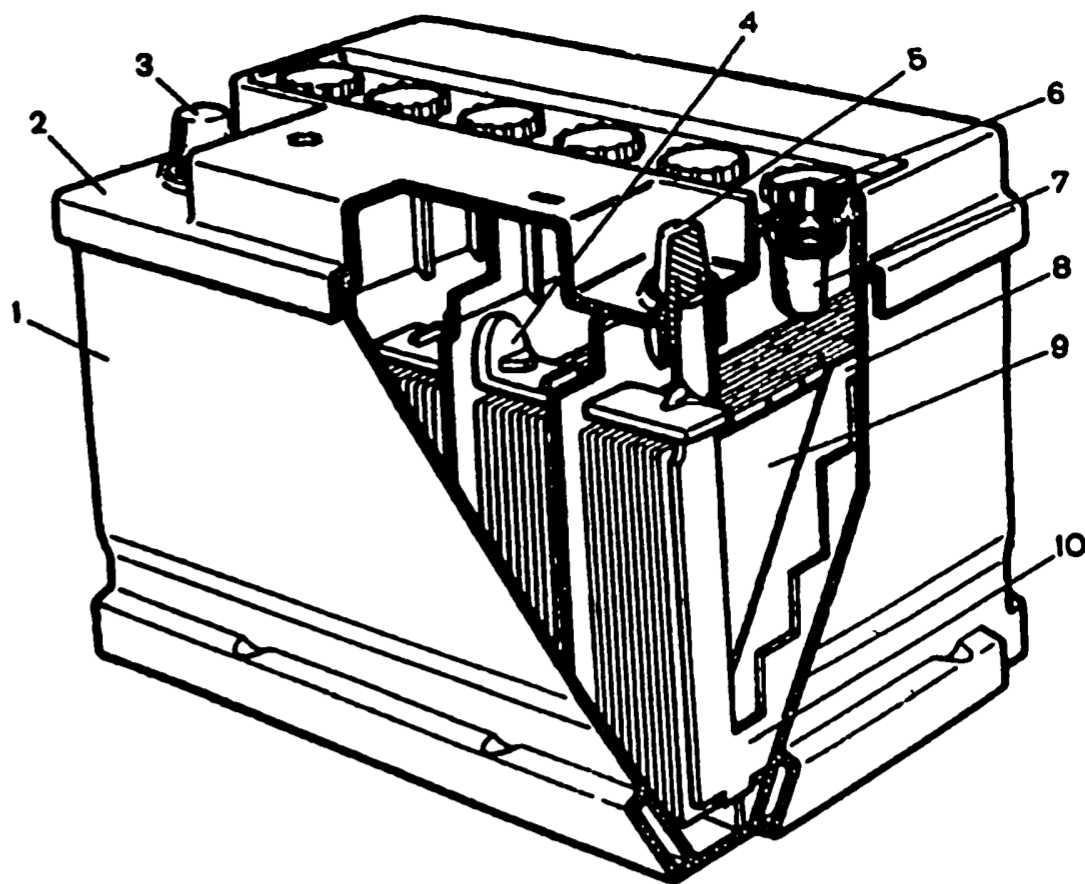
Разрез аккумуляторной батареи: 1 - корпус; 2 - крышка; 3 - положительный вывод; 4 - межэлементное соединение; 5 - отрицательный вывод; 6 - пробка; 7 - индикатор для проверки уровня электролита; 8 - сепаратор; 9 - положительная пластина; 10 - отрицательная пластина
